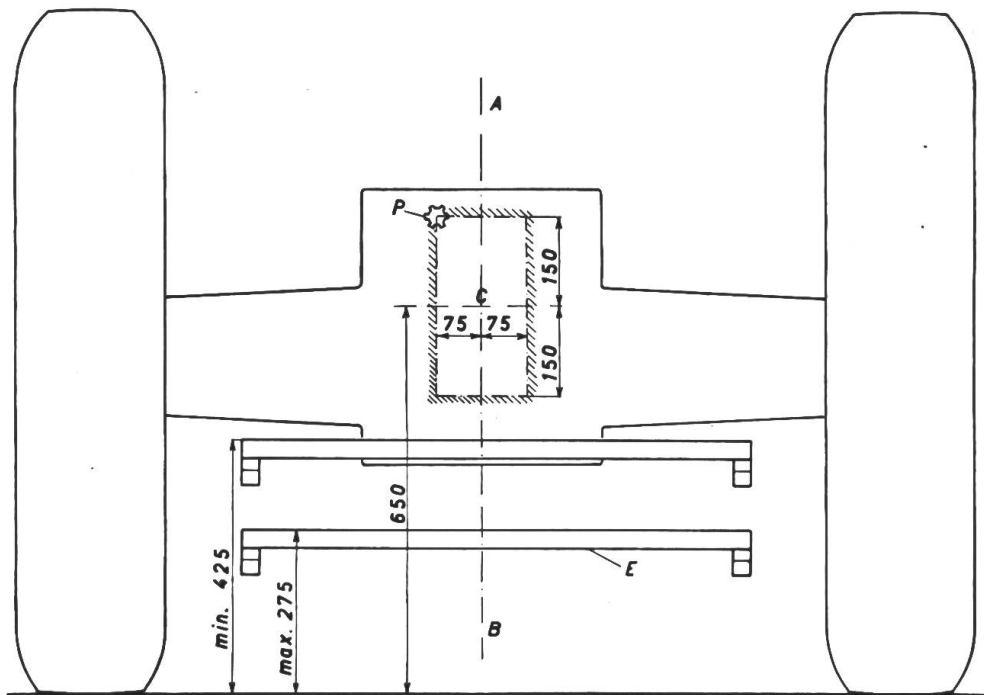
Emplacement de la prise de force par rapport au plan d'appui et au plan médian longitudinal et vertical du tracteur (cotes en mm).
